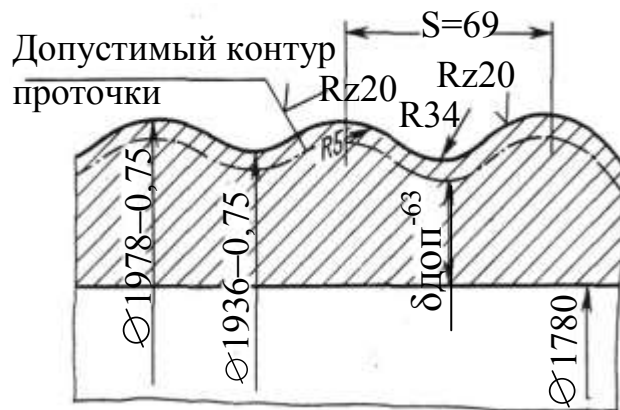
Ремонтный чертеж восстановления проточкой ручьев барабана
